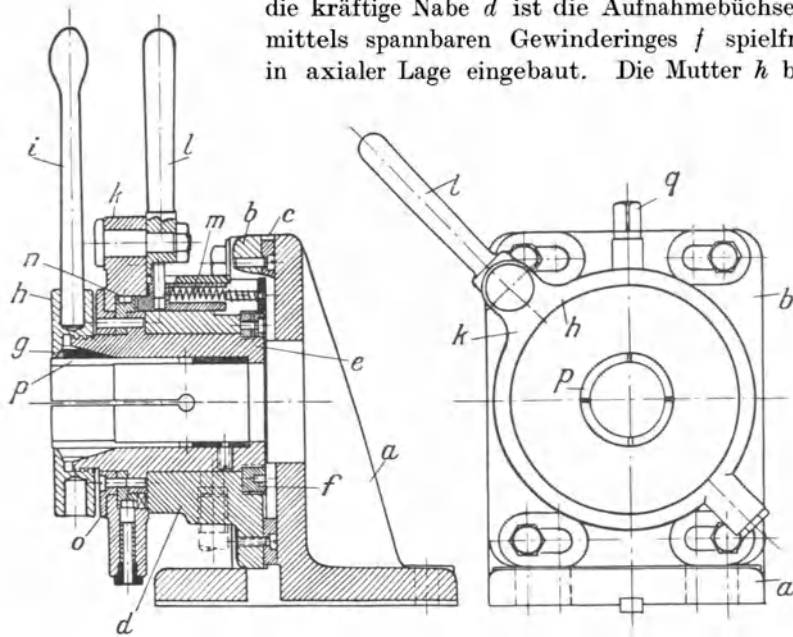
Fräsvorrichtung mit Teileinrichtung.
